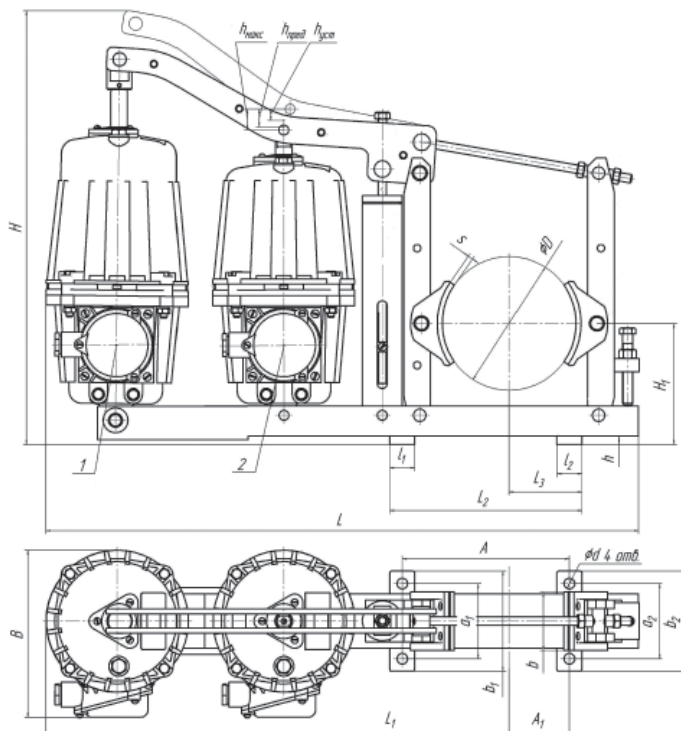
Общий вид с основными размерами тормозов типа ТКГ с дублированным приводом
